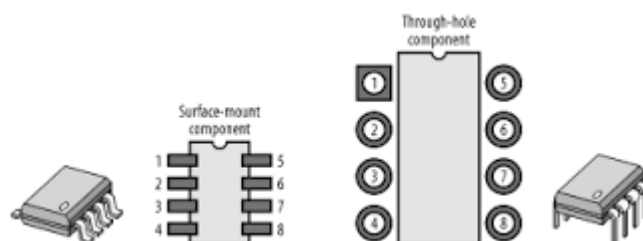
16 Diferencia de dimensiones, de un mismo tipo componente, para montaje superficial (izquierda) y para orificio pasante (derecha).
